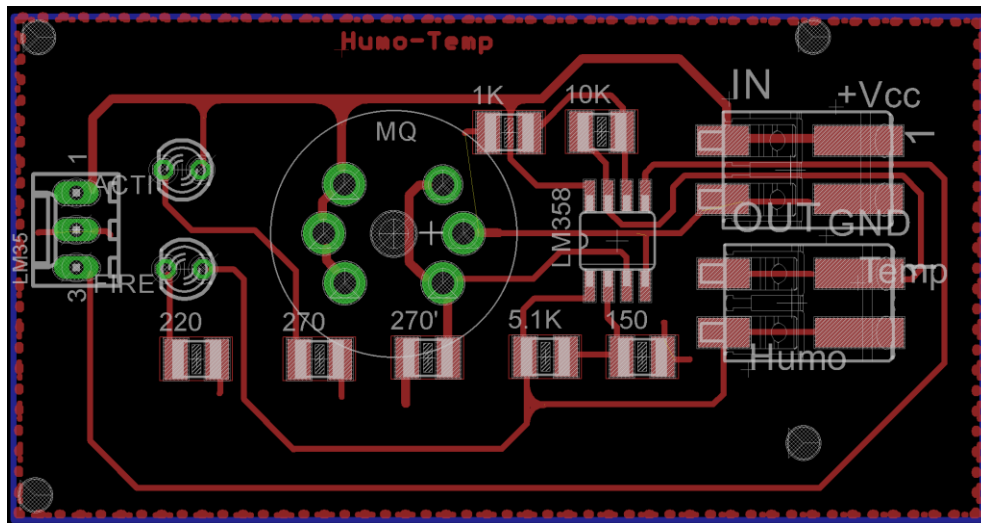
Diseño de PCB de módulo de humo y temperatura
